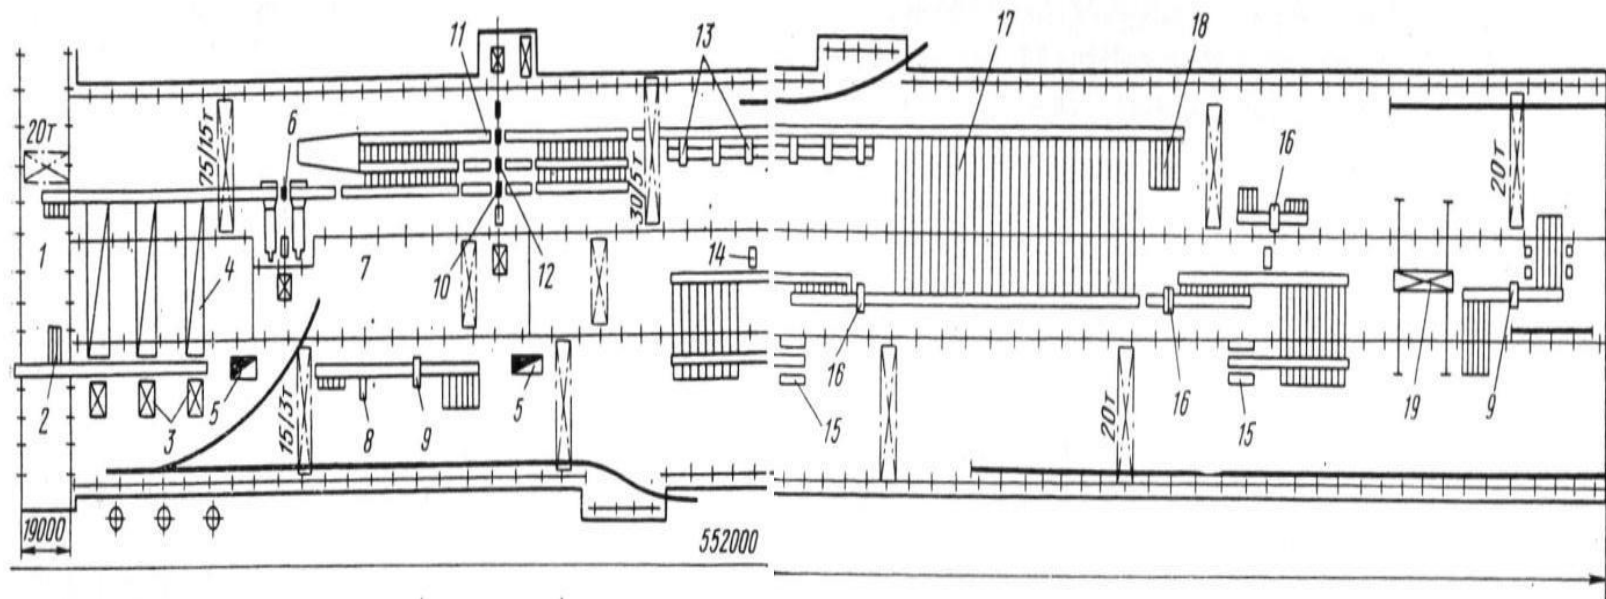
Схема розташування обладнання крупносортового стану 650: 1 – склад блюмів; 2 – завантажувальні решітки; 3 – товкачі; 4 – нагрівні печі; 5 – колодязь для окалини; 6 – чорнова двовалкова реверсивна кліть 800; 7 – електромашинна зала; 8, 14 – дискові пили холодної різки; 9 – правильний прес; 10, 12 – чорнові тривалкові кліті 650; 11 – чистова двовалкова кліть 650; 13 – дискові пили; 15 – укладчик готового прокату; 16 – правильні машини; 17 – холодильник; 18 – стелаж для якісних заготовок; 19 – передаточний візок
